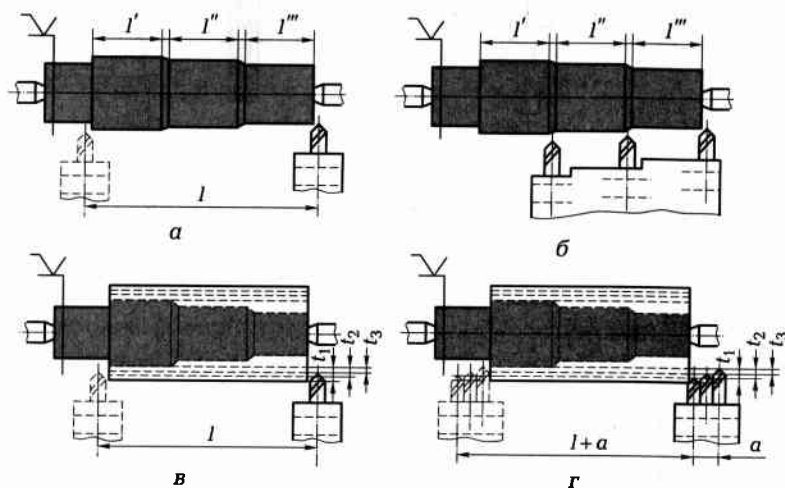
Схемы обработки наружной поверхности ступенчатого вала: а — на универсальном токарном станке; б — на многорезцовом токарном станке; в — за несколько рабочих ходов; г — с применением нескольких резцов
